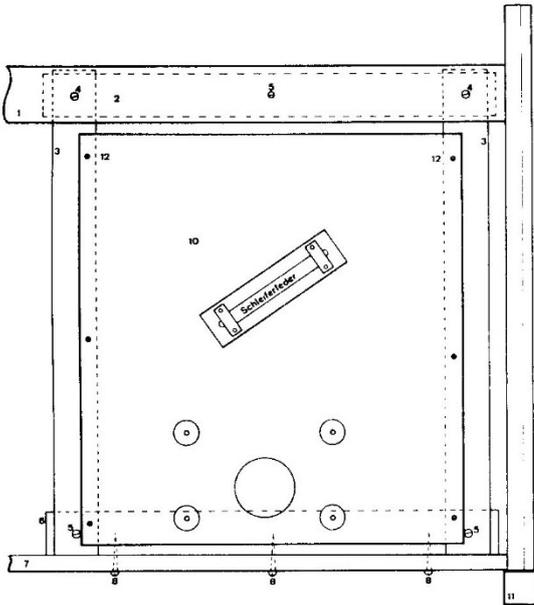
Einbau des Fußschwellers und des Schwellerkastens
